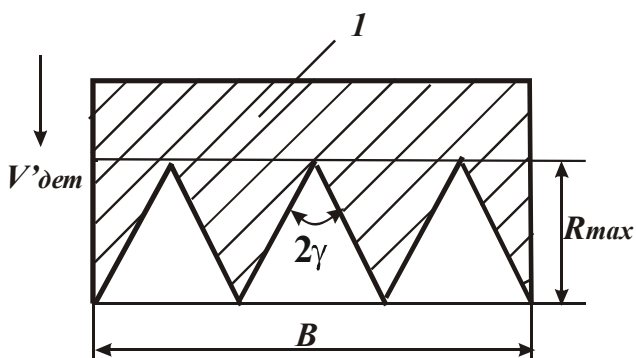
Схема образования шероховатости поверхности: 1 – обрабатываемый материал.
